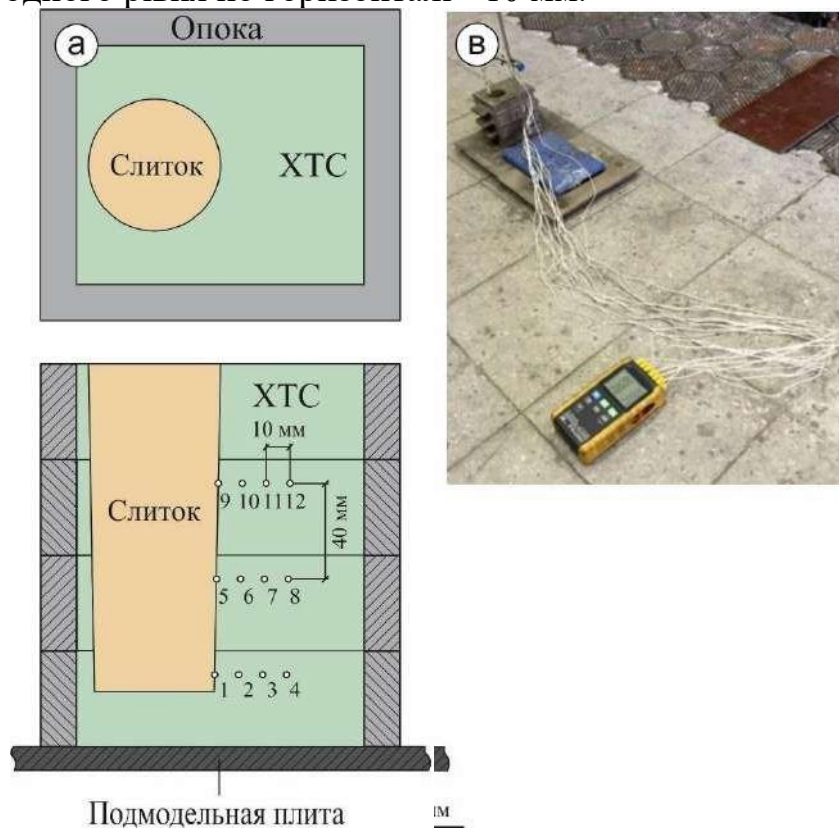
Схема форми з ХТС і загальний вигляд зібраної форми; а) для заливання сплавів Al-7Si; в) загальний вигляд зібраної форми з ХТС зі встановленими термопарами
